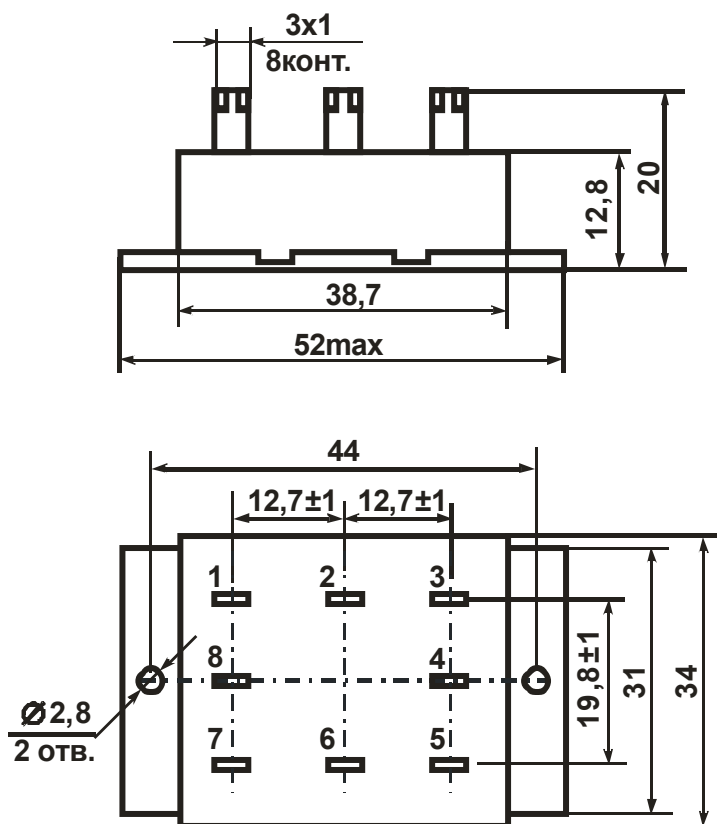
Габаритный чертёж модулей ВМ
